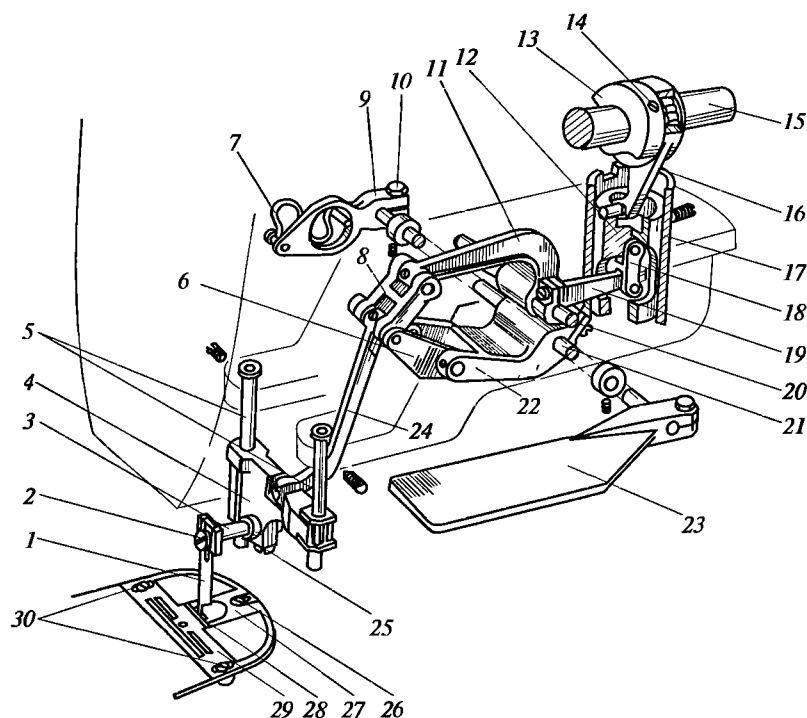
Схема механизма для обрезки края материала на швейной машине класса 131-121+100
